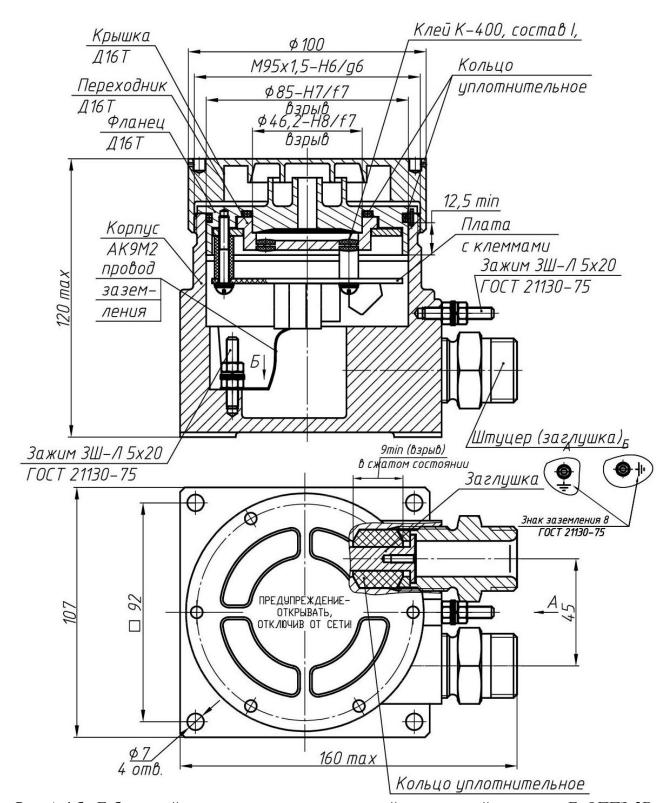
Габаритный чертёж звуковых оповещателей повышенной мощности ExOПП3-2B-ПМ-A и ExOПП3-2B-ПМ-220-A в алюминиевом корпусе (вариант), совмещённый с чертежом взрывозащиты. Маркировка показана в п. 1.6
